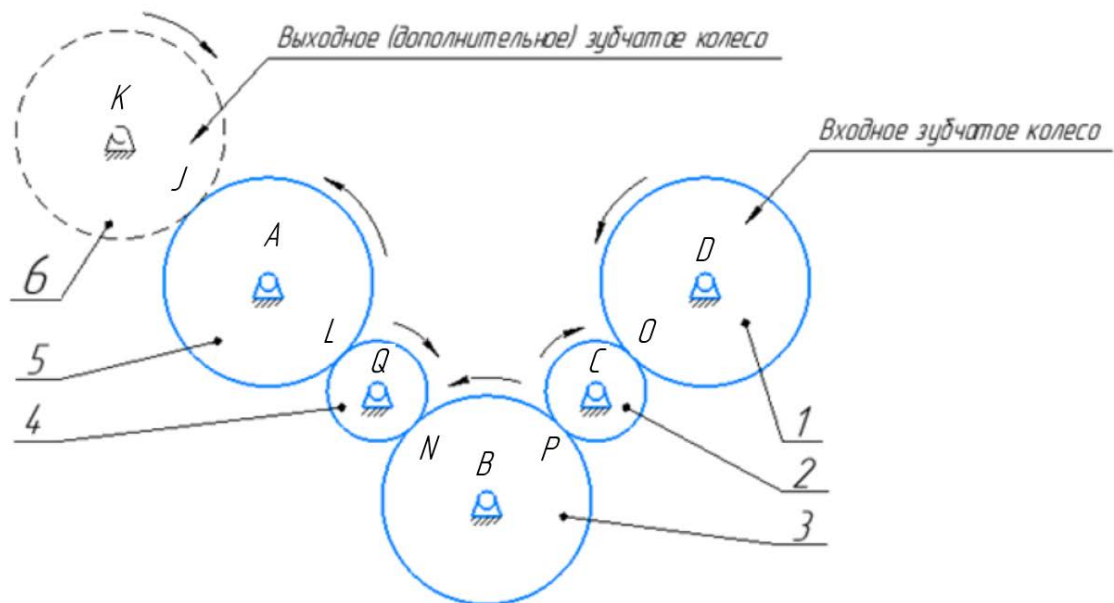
Рядовая прямозубчатая пятиступенчатая передача механизма с дополнительным зубчатым колесом⁴
